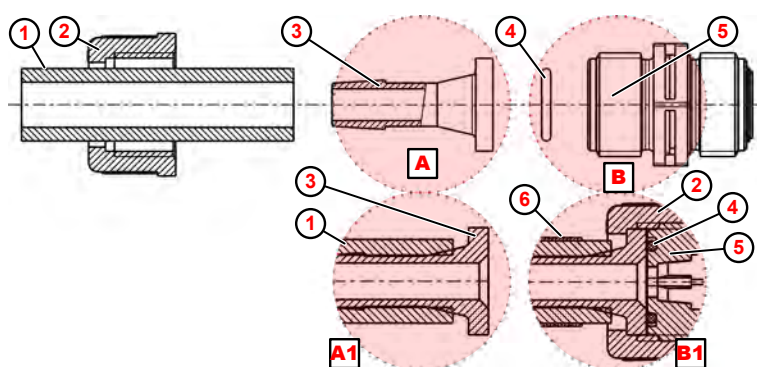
Raccord de conduit et flexible avec embout et collier de serrage
